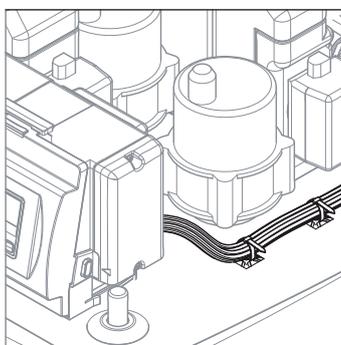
8. Fissare i cavi al serbatoio ad accumulo.
